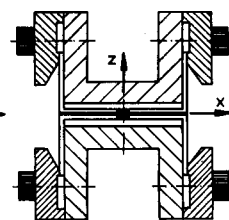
Belastungsprinzip der punkgeschweißten Blechprobe.
